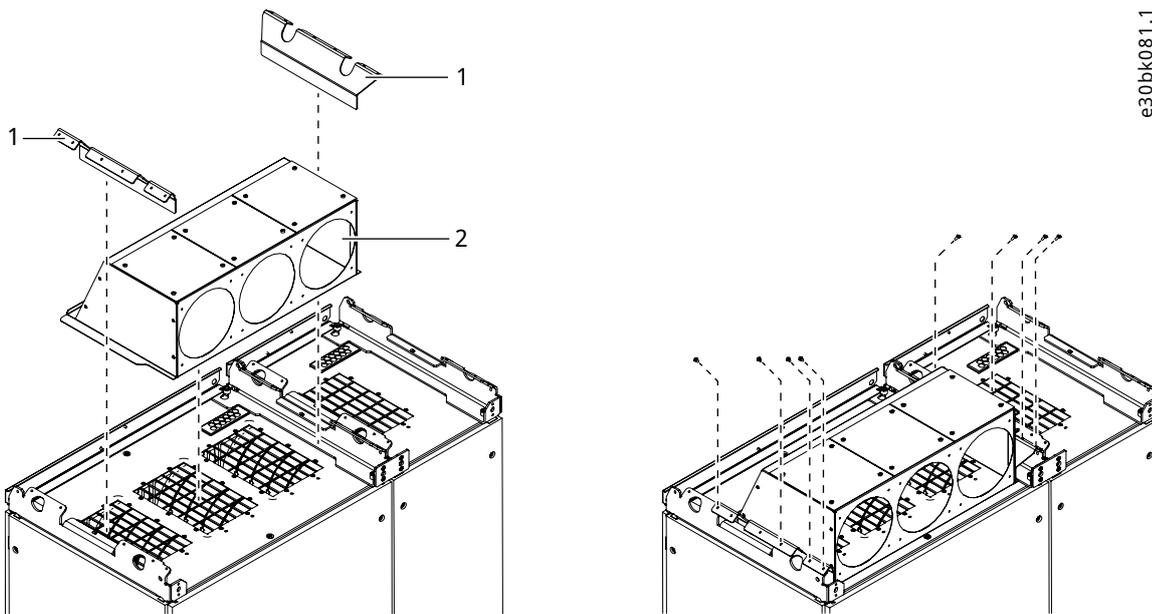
Installieren der Abdeckplatte bei der Option Rückseitiger Kühlluftkanal
